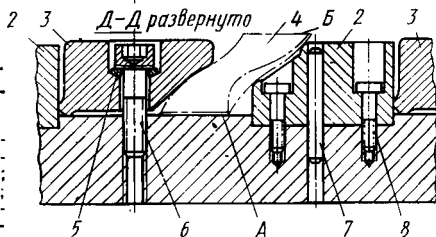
Многочастное приспособление для точения литых заготовок лопаток диафрагм:
